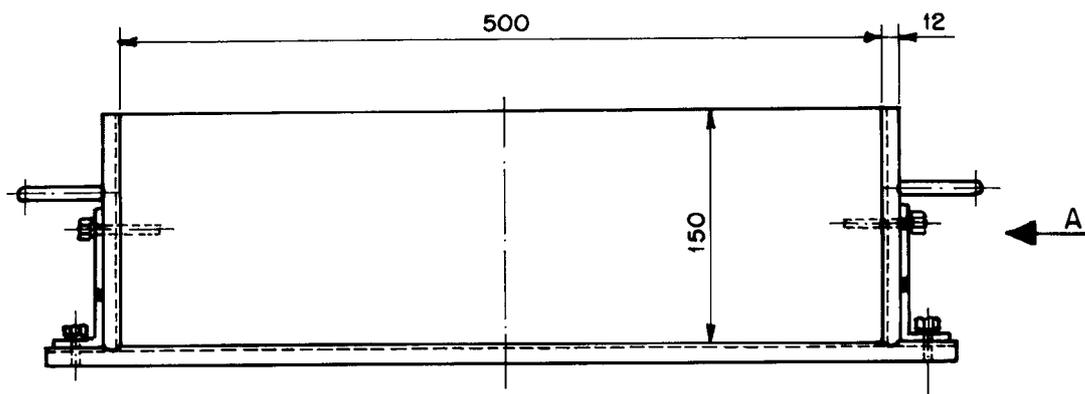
Molde cilíndrico de dimensão básica 150 mm
